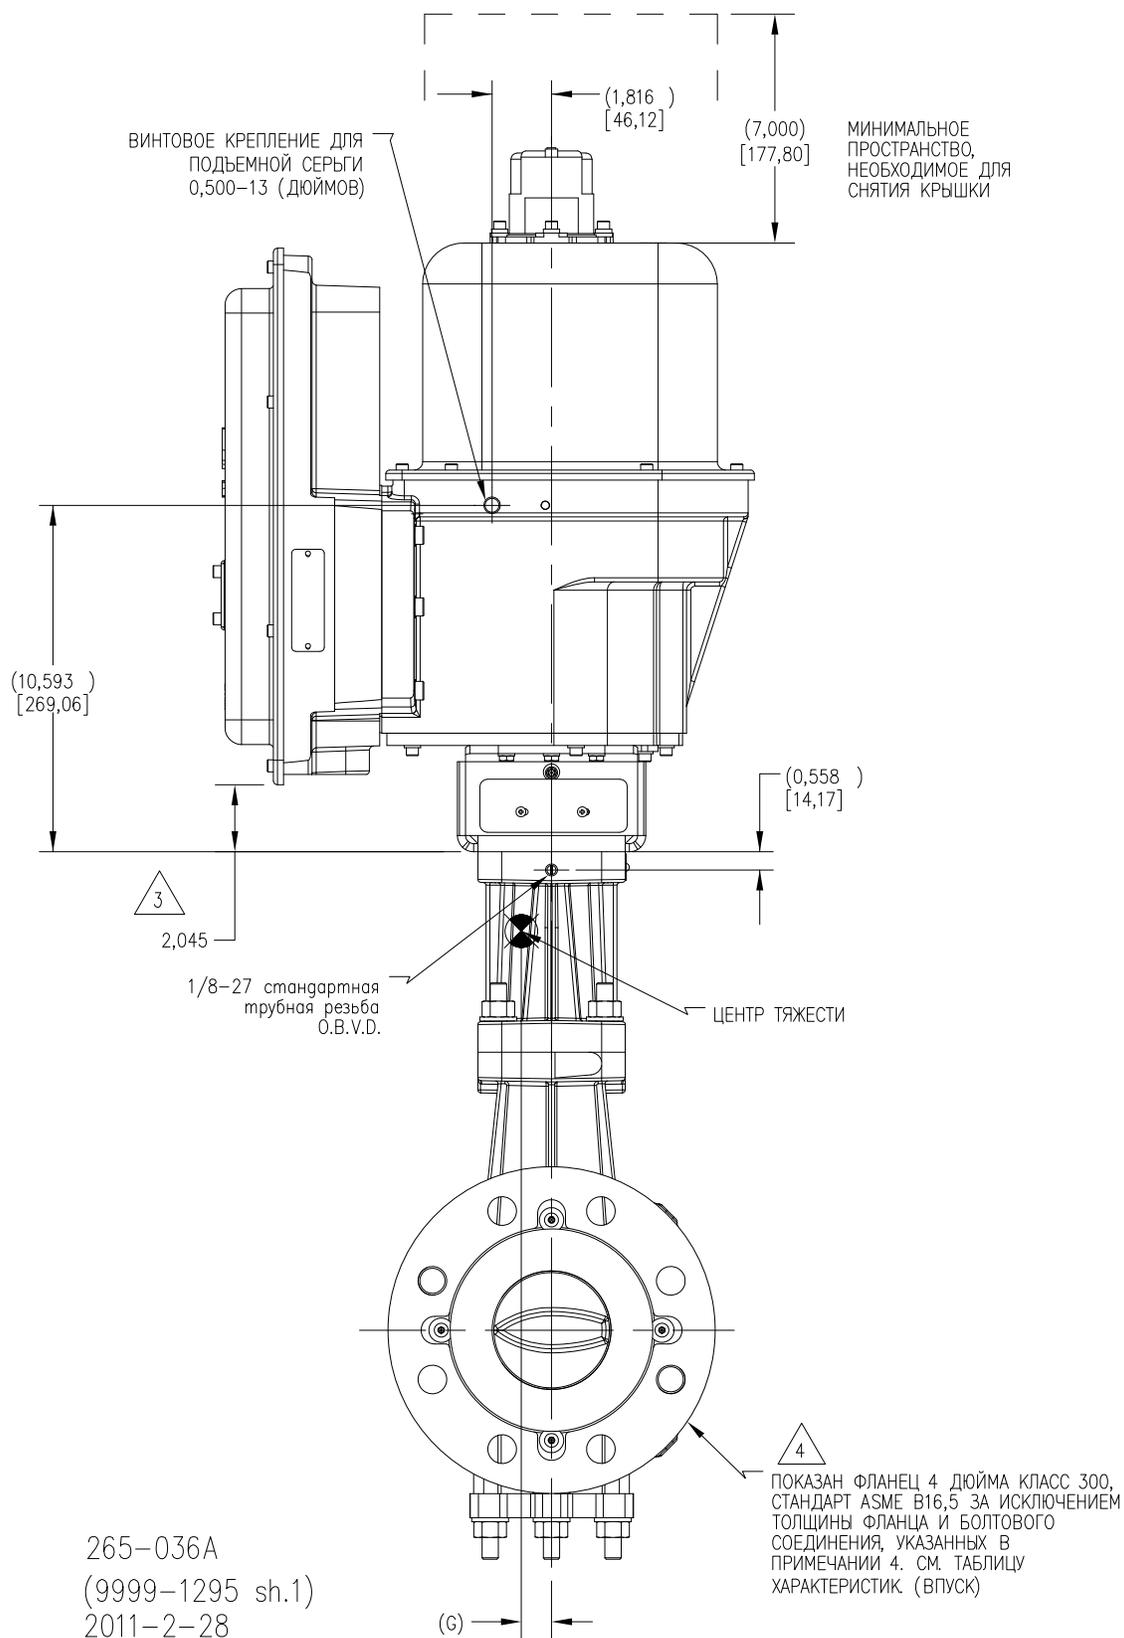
с. Габаритно-присоединительный чертеж RVP-200
